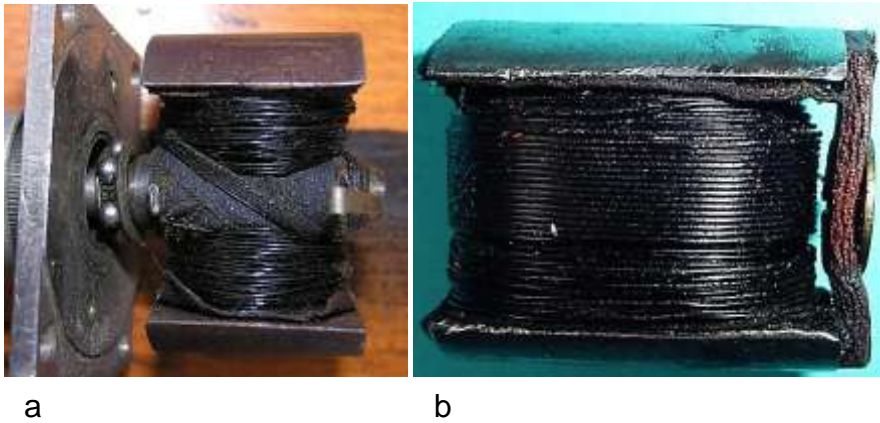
Mit Bitumenlack bewickelte Anker:
